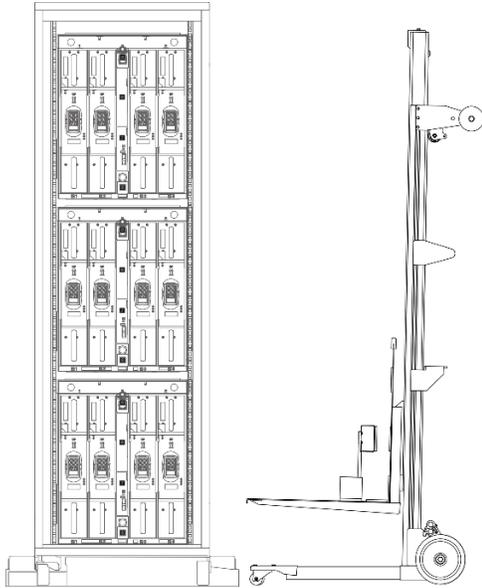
Mise en place de l'assemblage d'outil de levage à l'arrière de l'armoire
